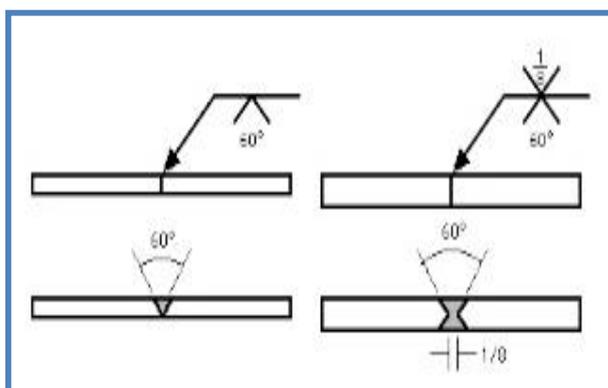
SOLDADURA DE RANURA
